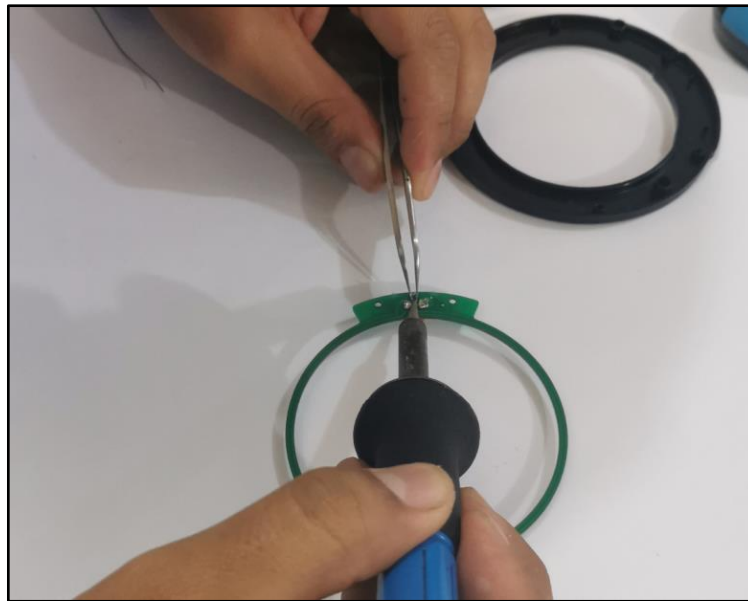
Proceso de soldado del chip tag y transponder SL2S2002
